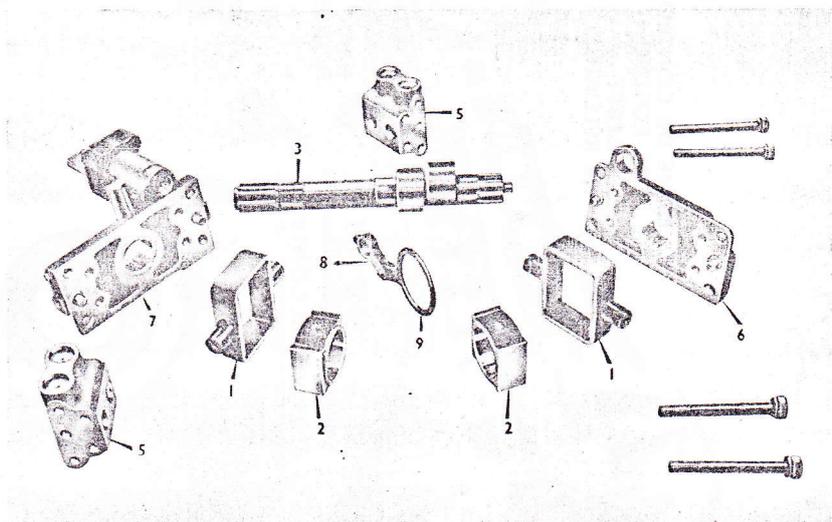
PIÈCES COMPOSANTES DE LA POMPE HYDRAULIQUE.
